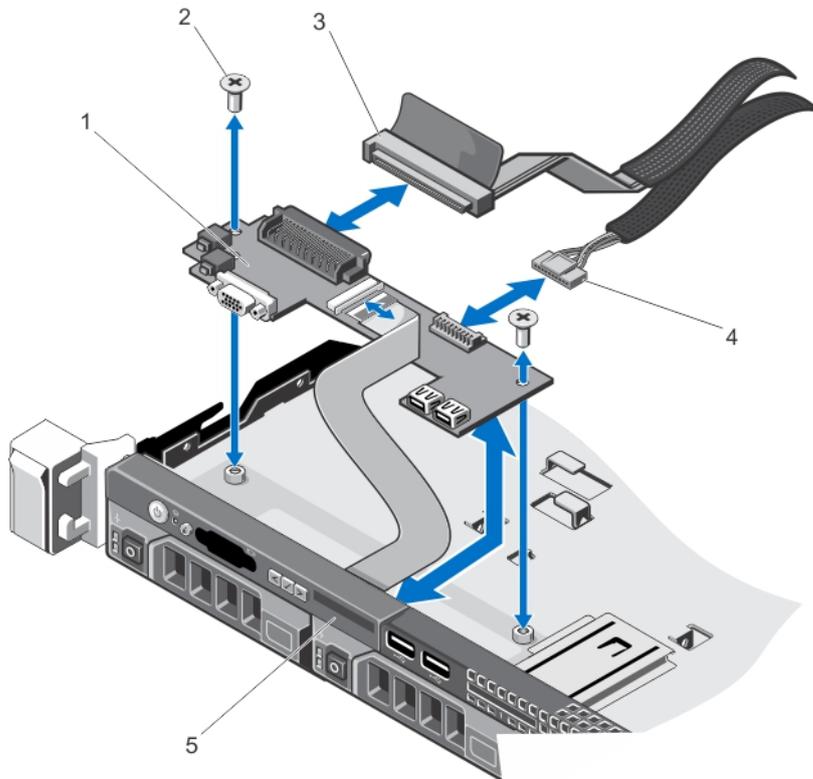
Entfernen und Installieren des Bedienfeldmoduls
